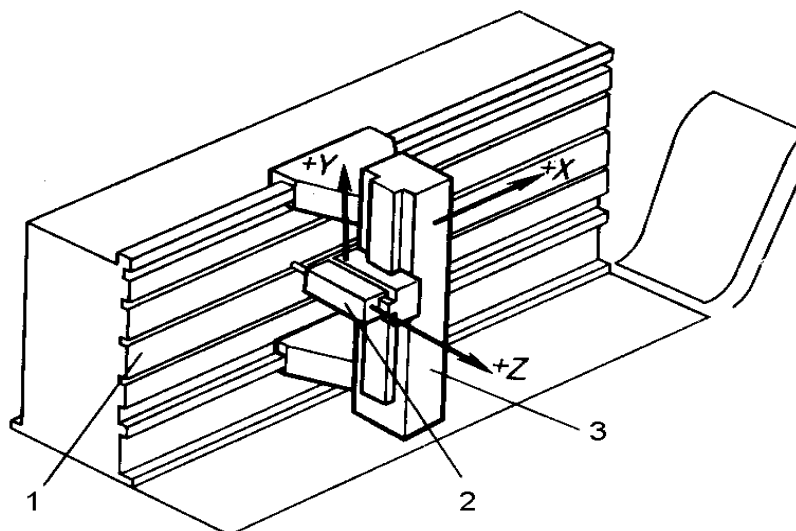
Компоновка станка для высокоскоростной обработки
